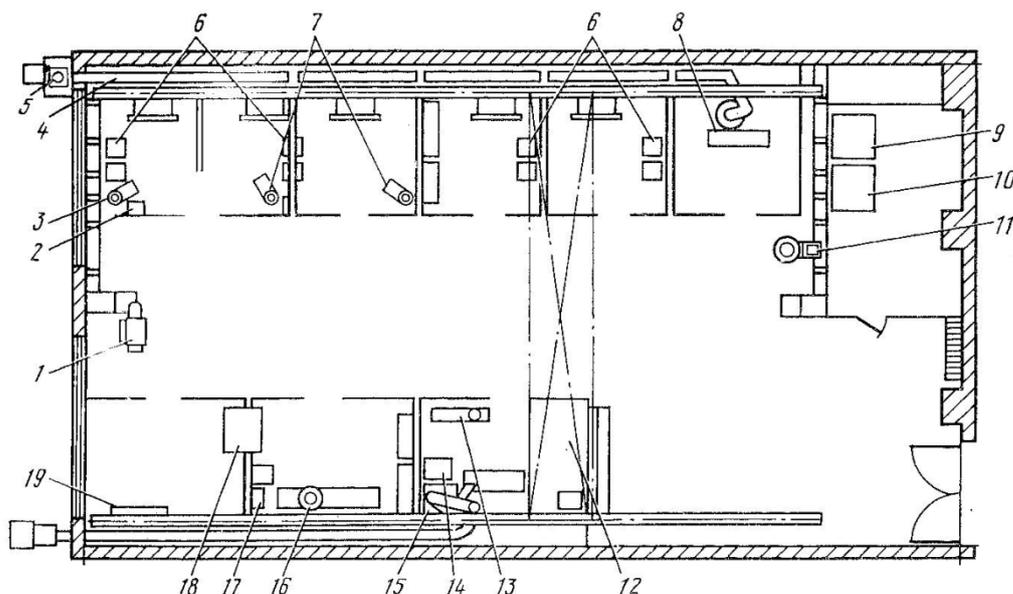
План электросварочного отделения: 1 – стенд для испытания шлифовальных кругов; 2, 14 – шкафы управления полуавтоматами; 3 – сварочный полуавтомат А-П97; 4 – вентиляционный воздухопровод; 5 – вентилятор; 6 – реостаты; 7, 13, 16 – сварочные аппараты; 8 – приспособление для наплавки триангелей; 9, 17, 18 – выпрямители; 10 – распределительный щит; 11 – сварочный генератор; 12 – кран-балка; 15 – трансформатор; 19 – стол сварщика.
